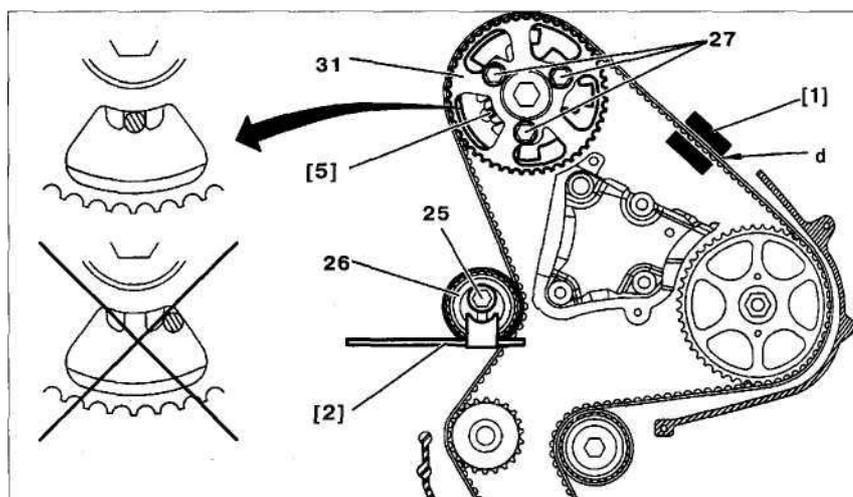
Установите приспособление [1] для измерения натяжения ремня ГРМ в точке «d». Прокрутите натяжной ролик 26 против часовой стрелки с помощью приспособления [2].
